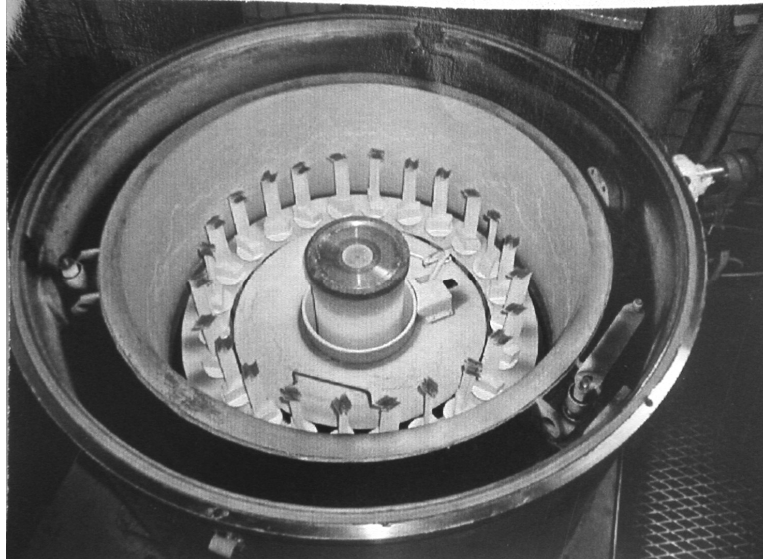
Лопатки ГТД в рабочей камере установки типа МАП
